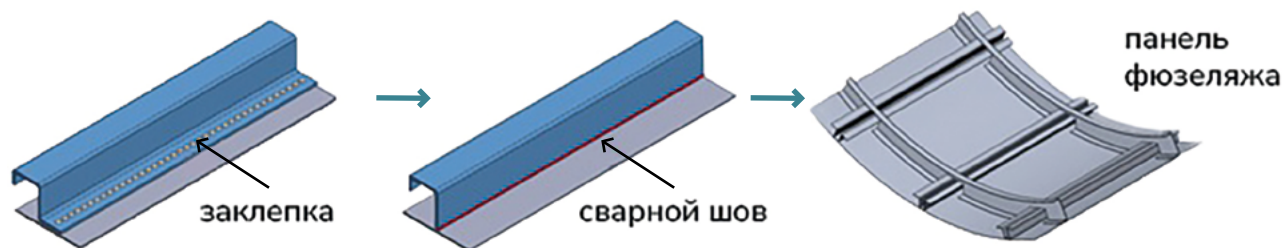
Эскиз крепления стрингера к фюзеляжу с помощью заклепочного соединения и лазерного сварного
